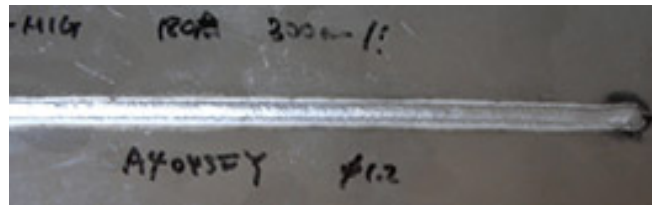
Cordón de soldadura MIG con arco pulsado, con Ar-O2 e hilo de 1,2mm de diámetro.
